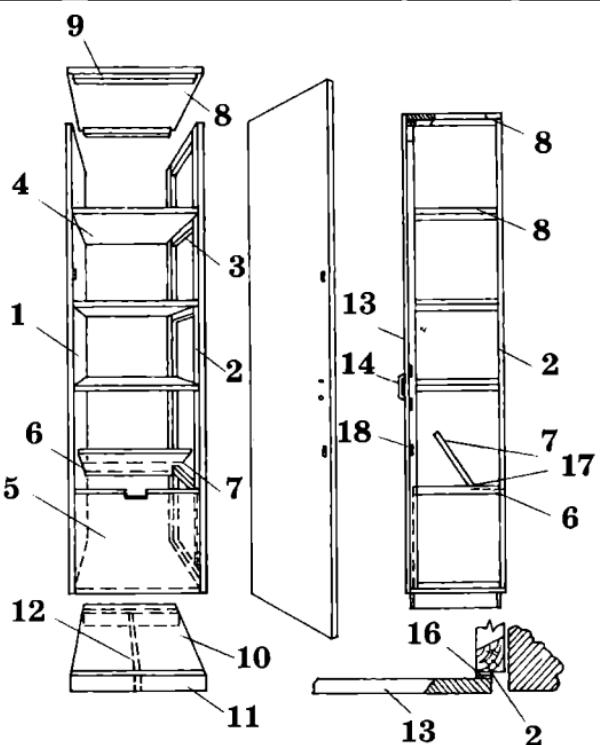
Сборка встроенного шкафчика для ванной комнаты: 1 — боковина; 2 — бруск продольный; 3 — бруск поперечный; 4 — полка; 5 — фасадная плита; 6 — полка с откидной крышкой; 7 — откидная крышка; 8 — верхняя крышка; 9 — поперечина; 10 — щит основания; 11 — бруск цоколя; 12 — доска средняя цокольная; 13 — дверка; 14 — дверная ручка; 16 — рояльная петля для дверки; 17 — рояльная петля для откидной крышки; 18 — магнитная защелка
